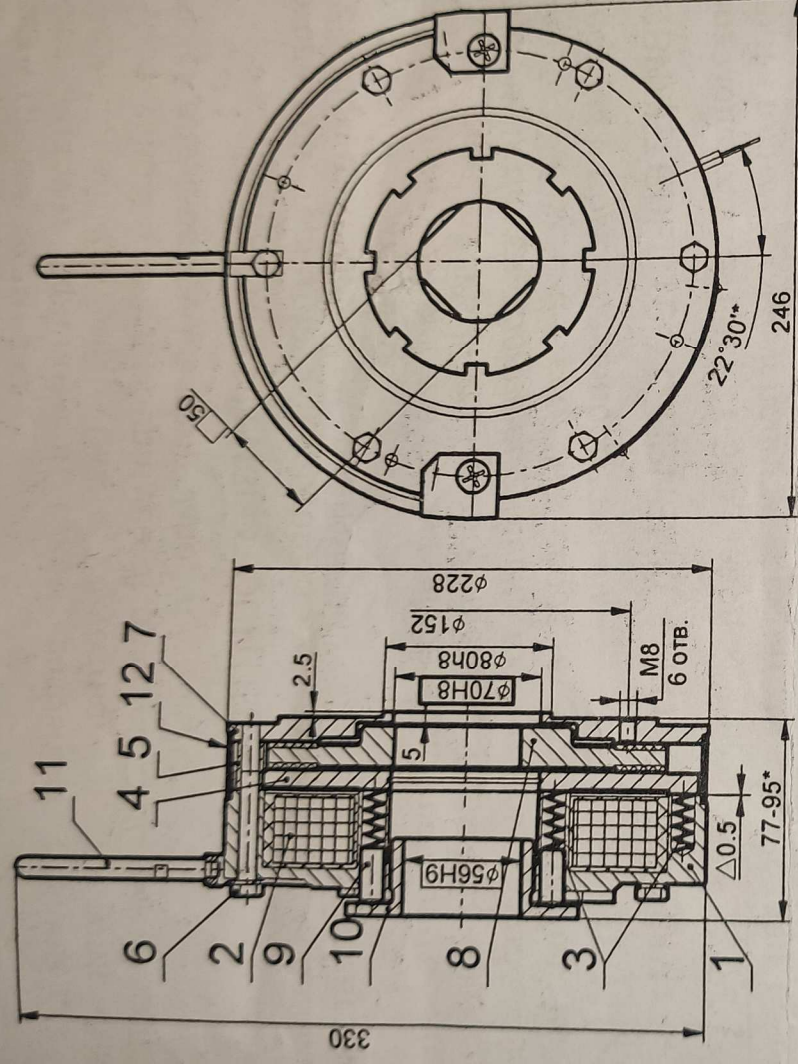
1 - корпус, 2 - эл.магнитная катушка, 3 - пружины, 4 - якорь, 5 - дистанционные втулки, 6 - винт, 7 - установочный диск, 8 - тормозной диск, 9 - толкатель, 10 - регулировочная гайка, 11 - рукоятка расфиксации, 12 - оболочка
